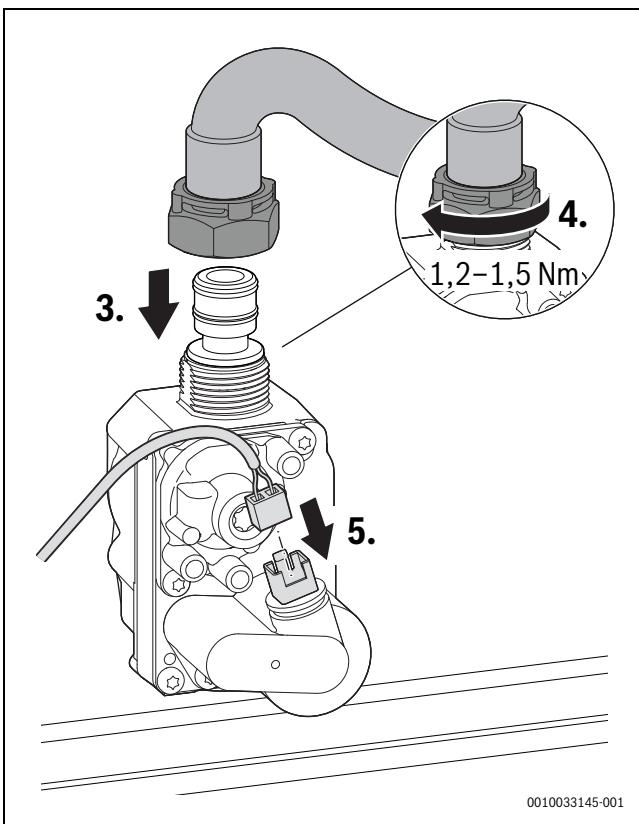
Gasschlauch und Stecker anschließen – Anzugsdrehmoment beachten
